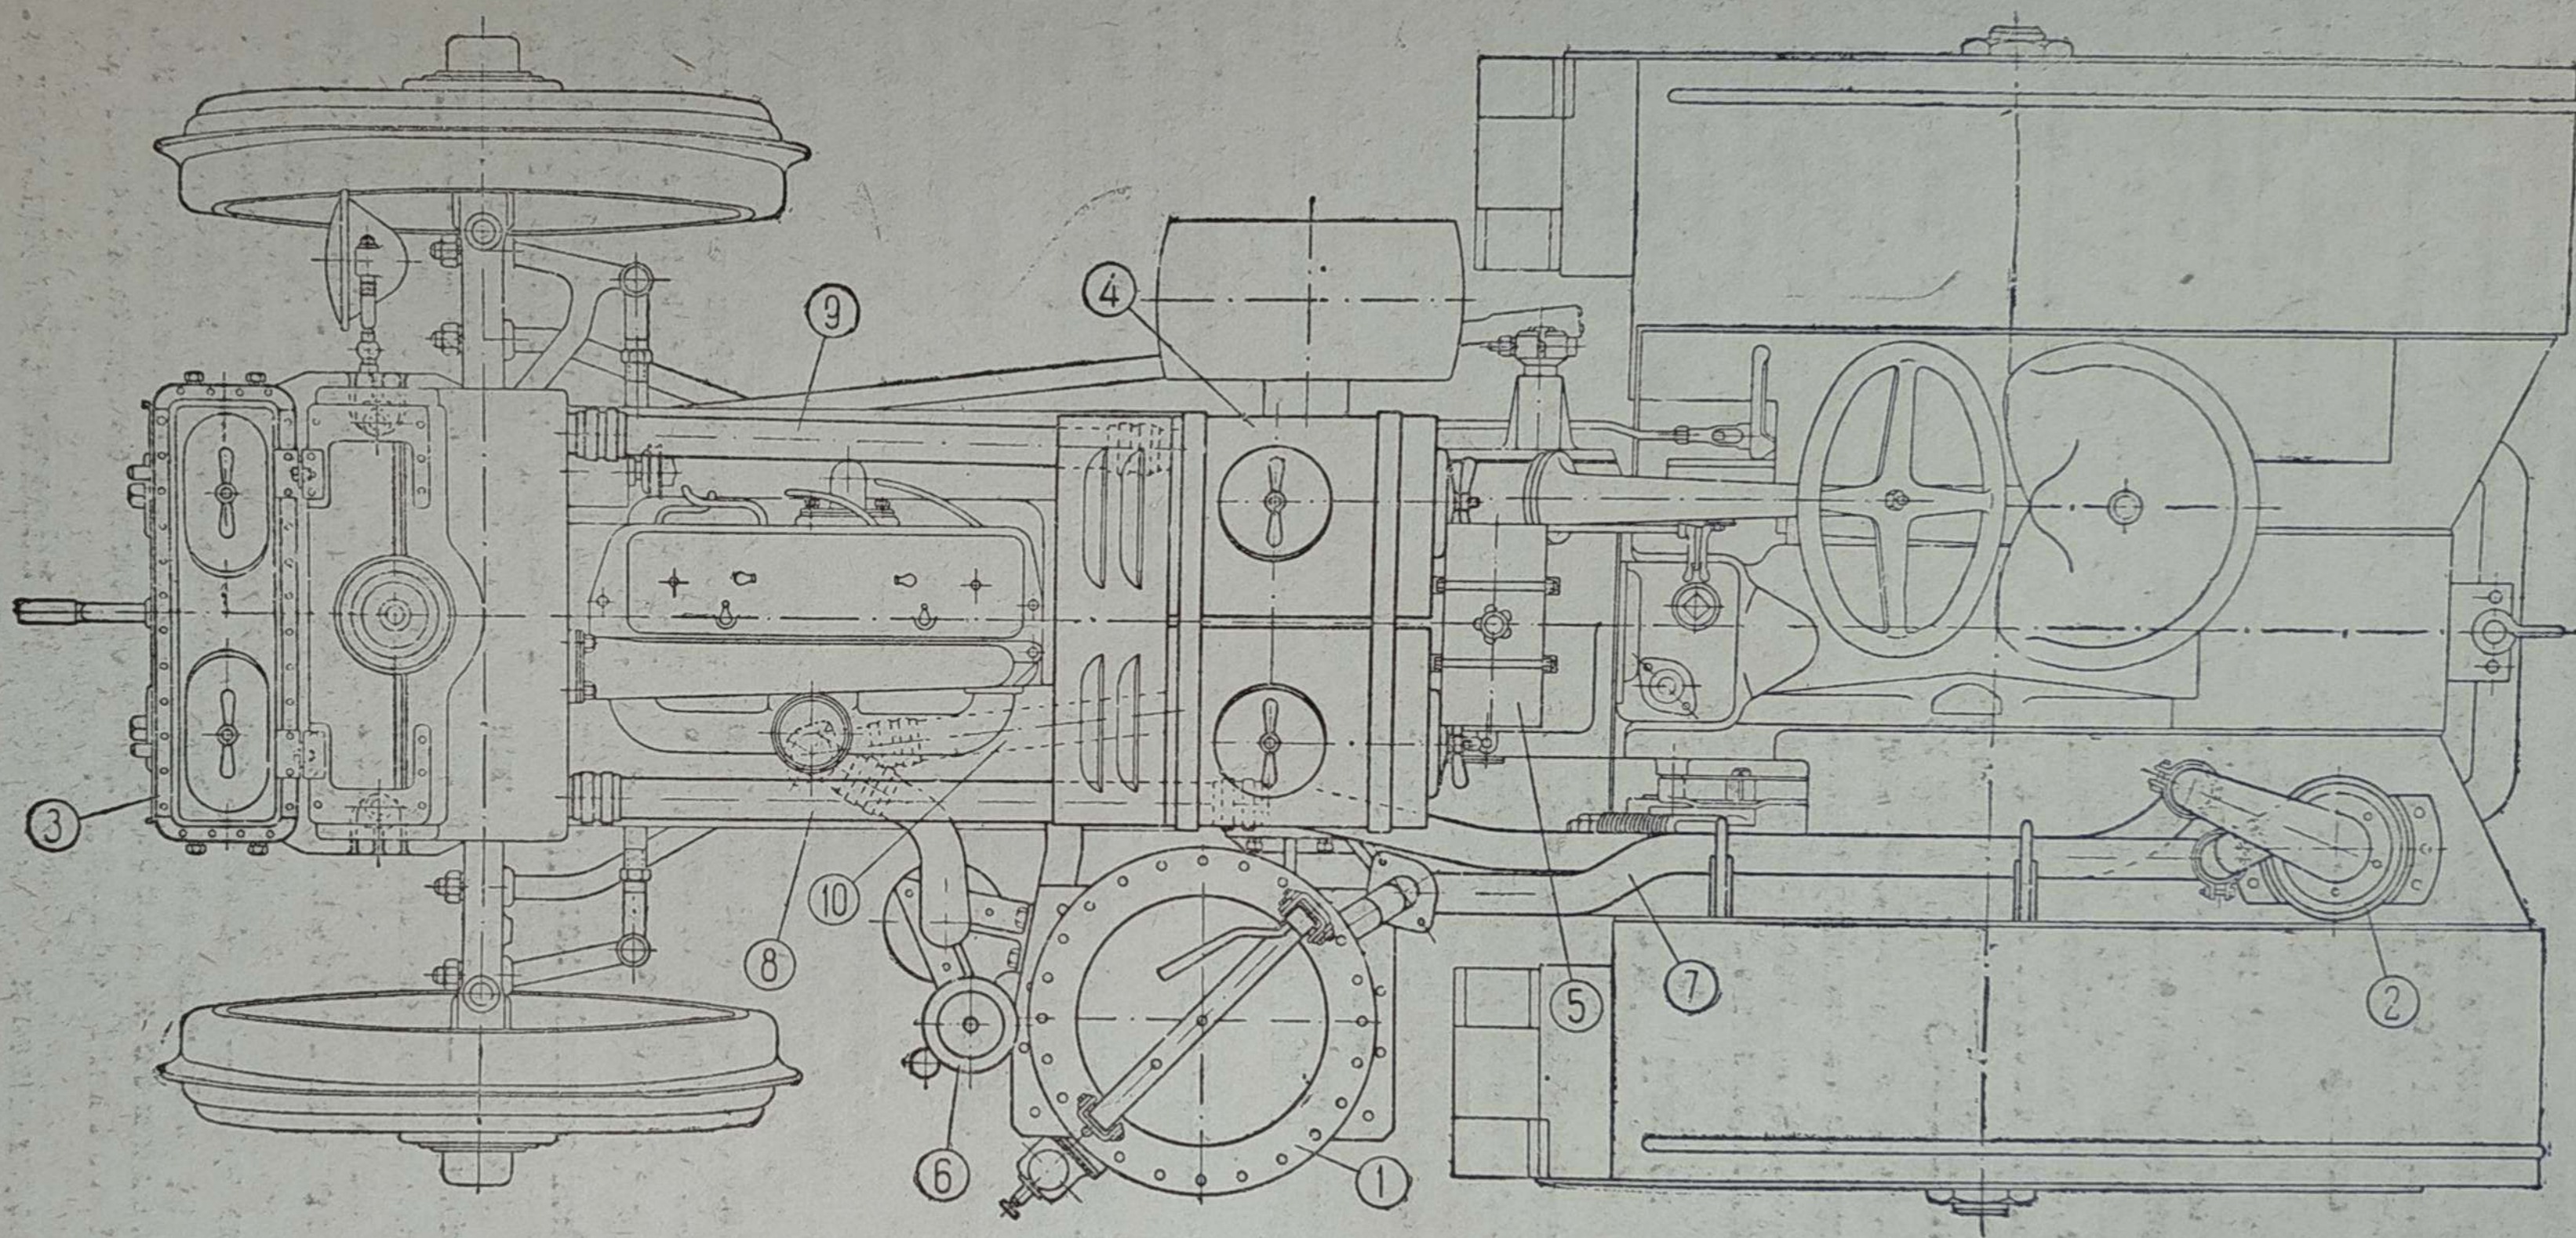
Общий вид колесного трактора СХТЗ-1 с газогенераторной установкой Г58У
